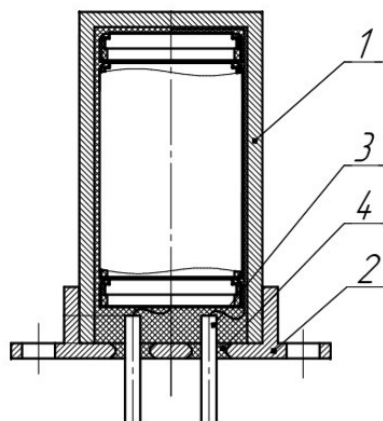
Общий вид размещенных в корпусе ЭОАИП
